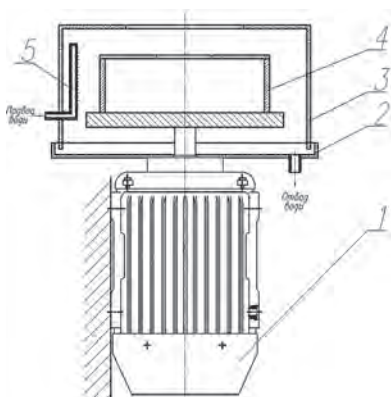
Схема экспериментальной установки центробежного литья с вертикальной осью вращения: 1 – электродвигатель; 2 – лоток для отвода охладителя; 3 – защитный кожух; 4 – форма для центробежного литья; 5 – охлаждающая форсунка
